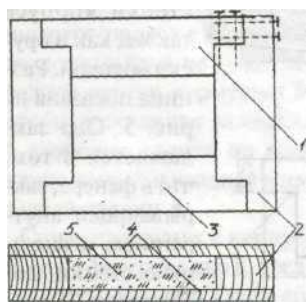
Боковая стенка корпуса в собранном виде (240х508 мм): 1 — верхний брусок; 2 — боковой брусок; 3 — нижний брусок; 4 — фанера; 5 — наполнитель
